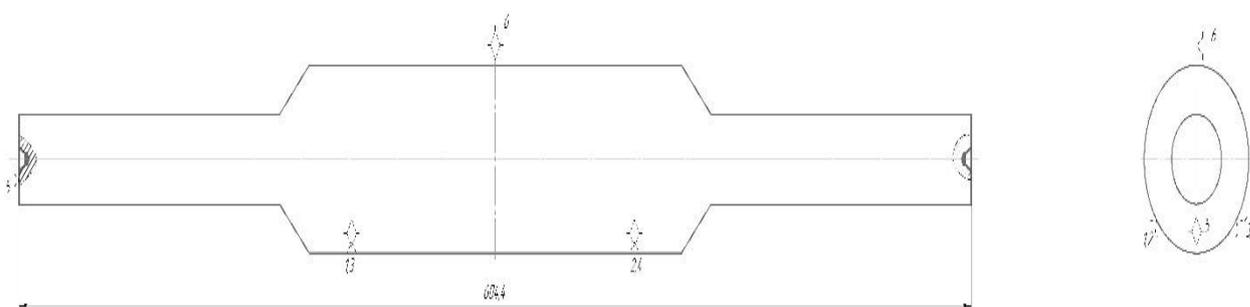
Схема базирования на фрезерно центровальная операция
